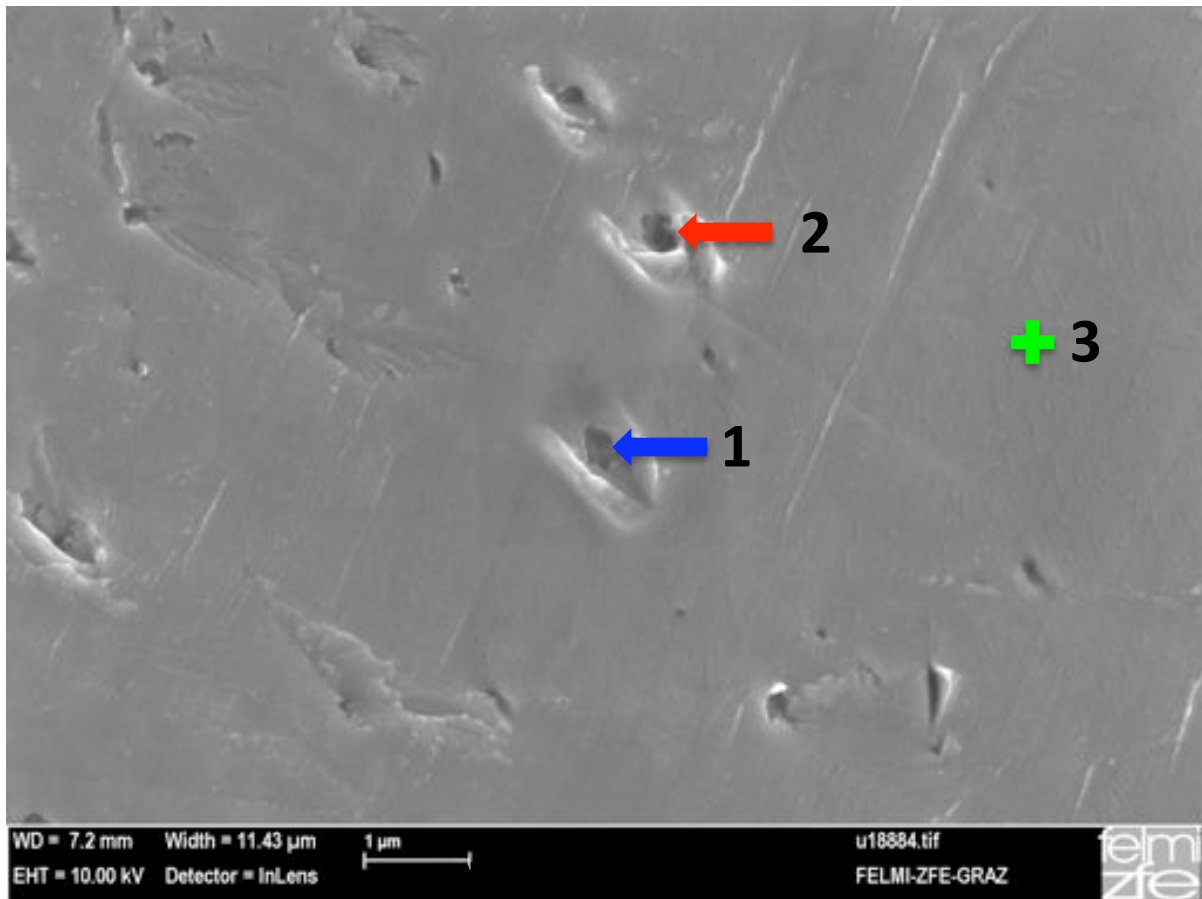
Ausschnitt der Bruchfläche von der Probe 2.14, Schweißprobe ohne Risse
